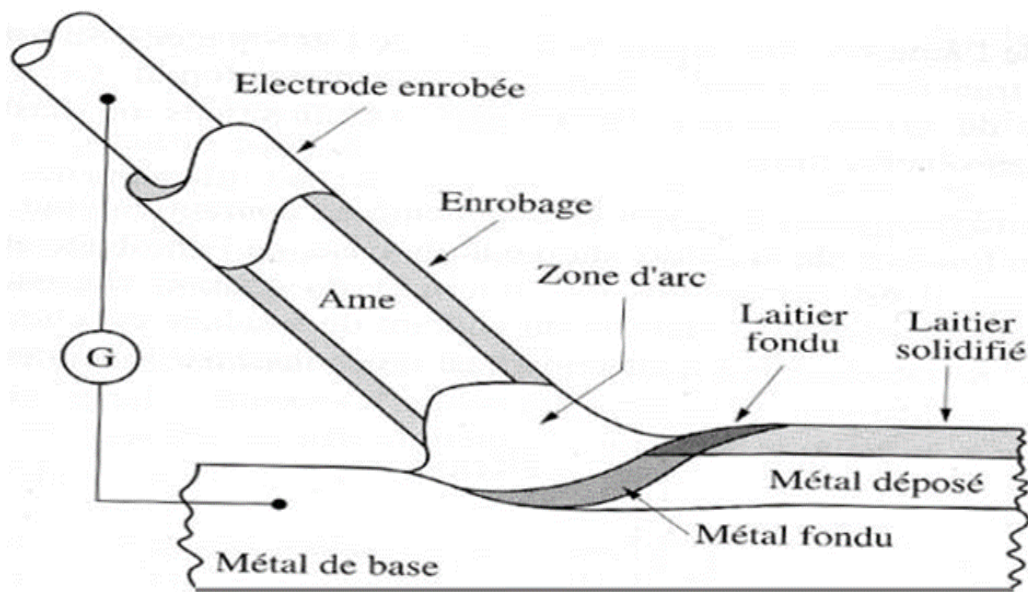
Electrode enrobée durant le soudage [12].
